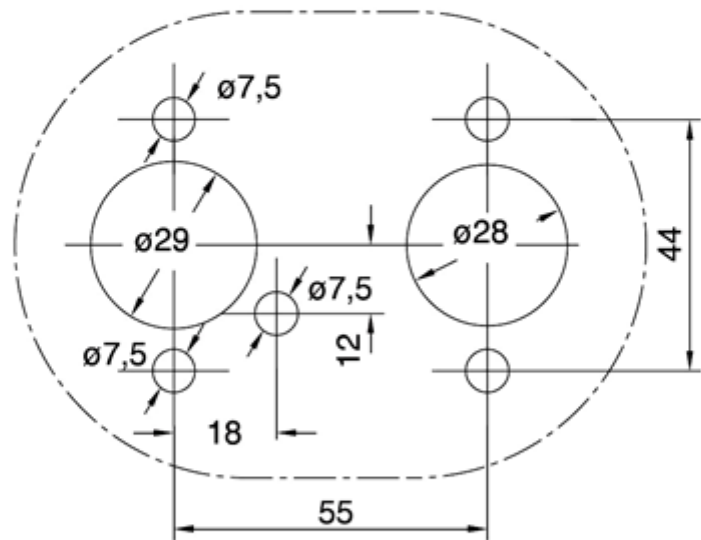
Габаритные и присоединительные размеры БПМ
